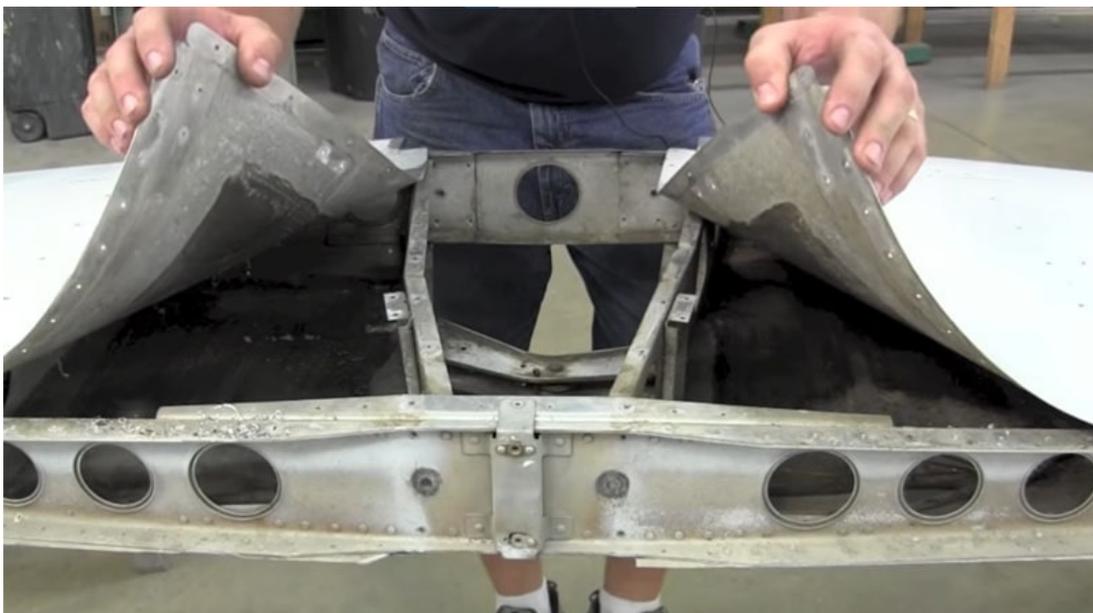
Inspección del interior de un estabilizador horizontal. Cessna
